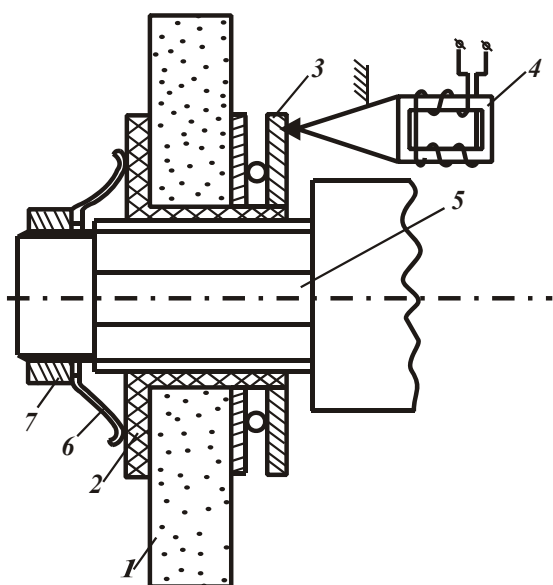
Устройство с осевым перемещением шлифовального круга: 1 – круг; 2 – шлицевая втулка; 3 – подшипник; 4 – магнестрикционная колебательная система; 5 – шлицевый вал; 6 – пружина; 7 – гайка.
